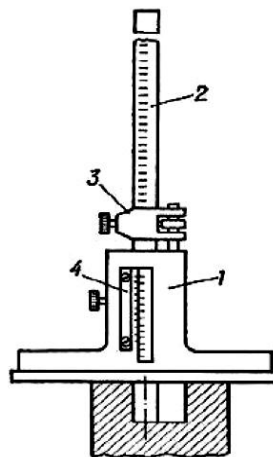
Загальний вигляд штангенглибиноміра
